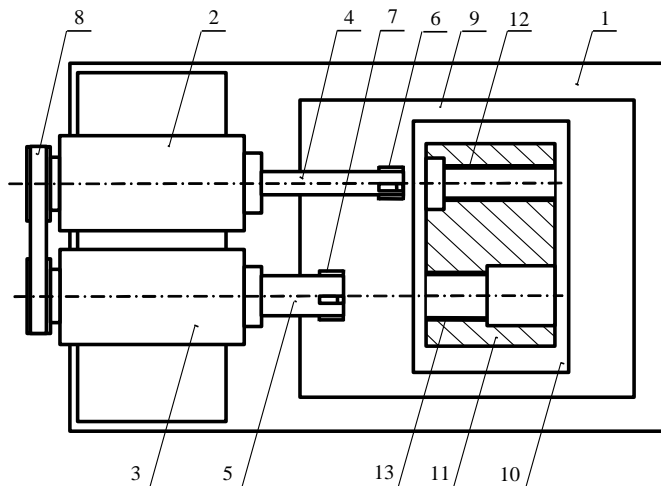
Схема обработки параллельных отверстий на ОРС: 1 – ОРС; 2 и 3 – отделочно-расточные головки; 4 и 5 – РИОР; 6 и 7 – режущие элементы РИОР; 8 – синхронный ремень; 9 – подвижный стол станка; 10 – приспособление станка; 11 – заготовка; 12 и 13 – обрабатываемые отверстия
